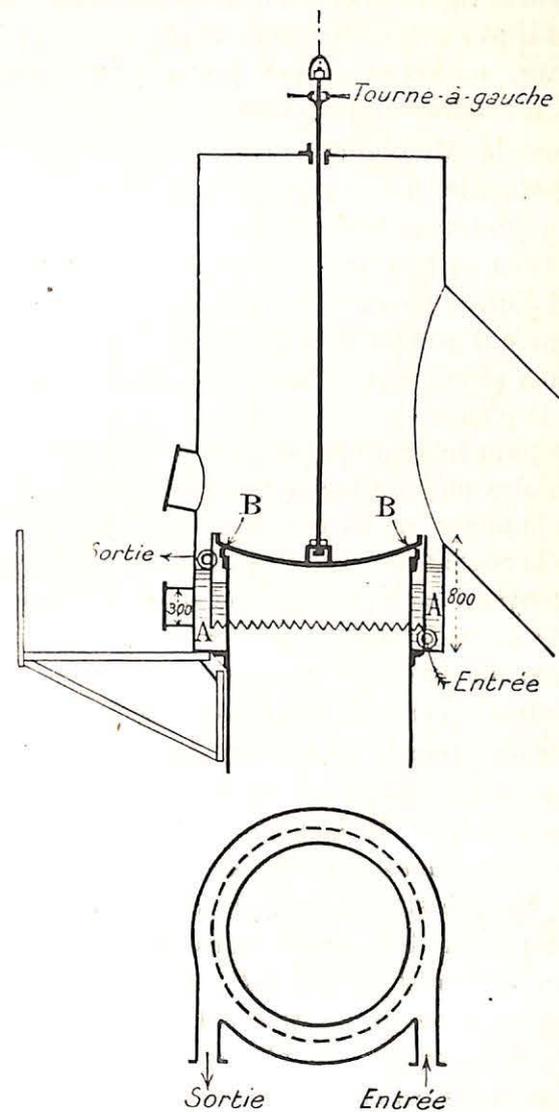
bis. — Cloche à joint hydraulique A et à joint métallique rodé B.
